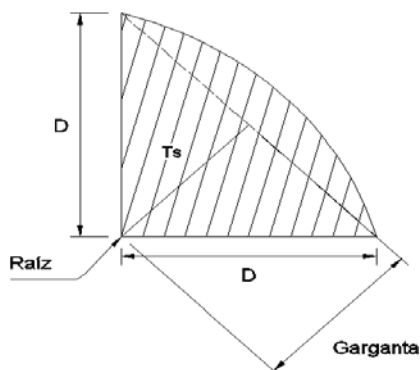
Geometría de la soldadura a realizar
